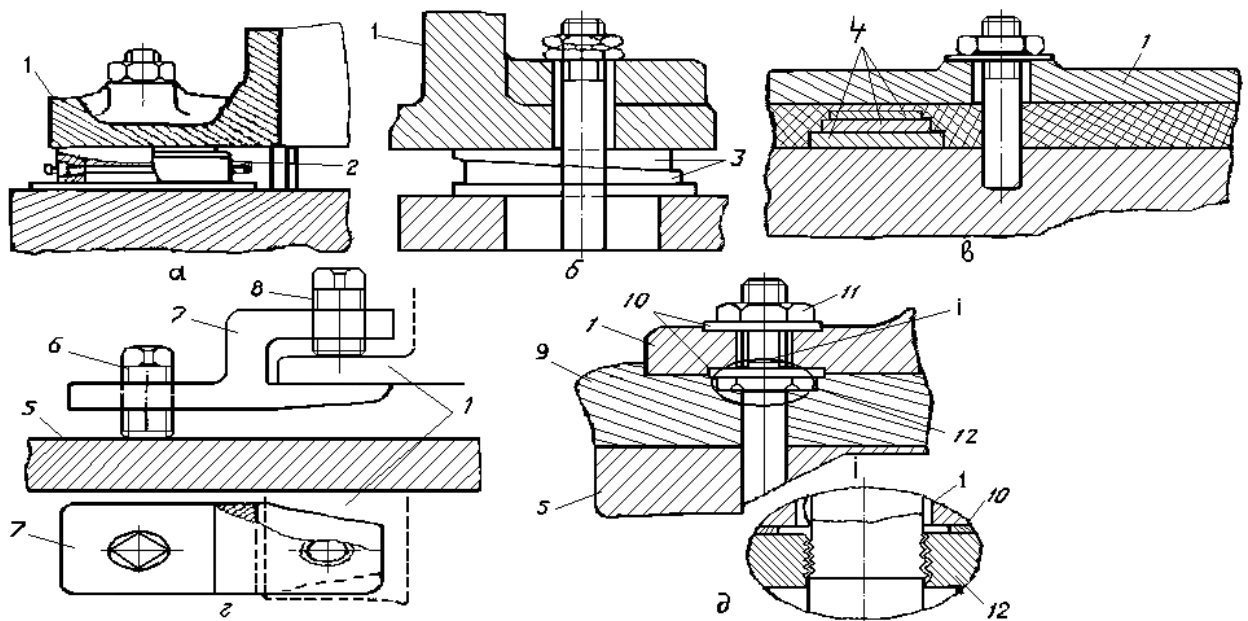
Схема кріплення обладнання на фундаментах і підставках:
